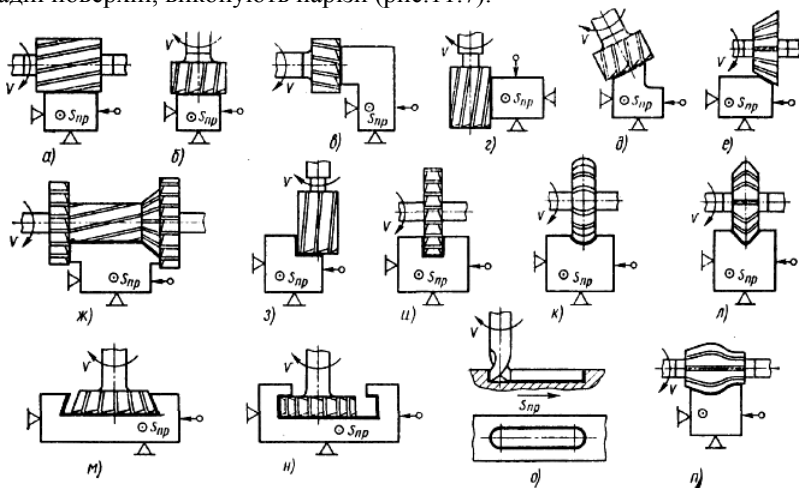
Фрезерні роботи: *а* – обробка горизонтальної поверхні циліндричною фрезою; *б* – обробка горизонтальної поверхні торцевою фрезою; *в* – обробка вертикальної поверхні торцевою фрезою; *г* – обробка вертикальної поверхні кінцевою фрезою; *д* – обробка похилої поверхні торцевою фрезою; *е* – обробка похилої поверхні дисковою кутовою фрезою; *ж* – фрезерування набором фрез; *з* – фрезерування уступу кінцевою фрезою; *и* – обробка прямокутного пазу дисковою фрезою; *к, л* – фрезерування фасонних канавок дисковими фрезами; *м* – обробка пазу типу ластівчиного хвоста пазовою фрезою;
